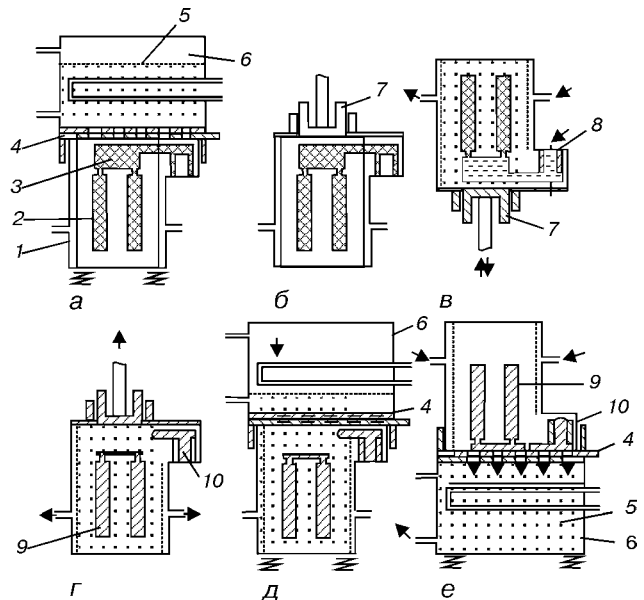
Схема ГАМОДАР-процесса: а — формовка; б — установка камеры прессования; в — заливка и выдавливание жидкого металла; г — удаление камеры прессования; д — подсоединение вспомогательного бункера; е — выбивание песка; 1 — контейнер; 2 — пенополистироловая модель; 3 — литниковая система; 4 — открытые жалюзи; 5 — песок; 6 — вспомогательный бункер; 7 — поршень; 8 — жидкий металл; 9 — блок отливок; 10 — литник
